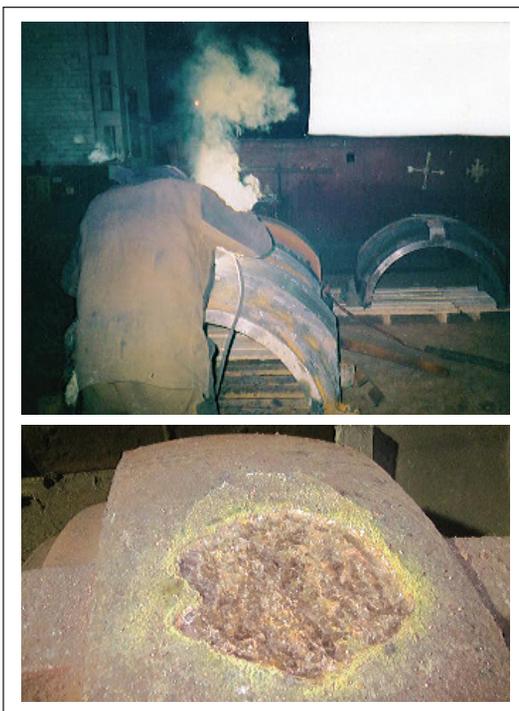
Сварка крышки подшипника. Электроды «Комсомолец»
